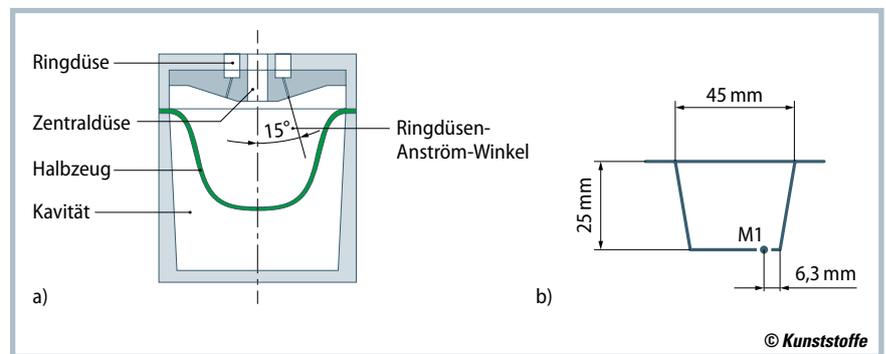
Druckluft-Negativumformen mittels FIT in einem rotationssymmetrischen Werkzeug: a) Versuchsaufbau, b) Formteilgeometrie und Position des Messpunkts (Quelle: Fraunhofer IVW)
